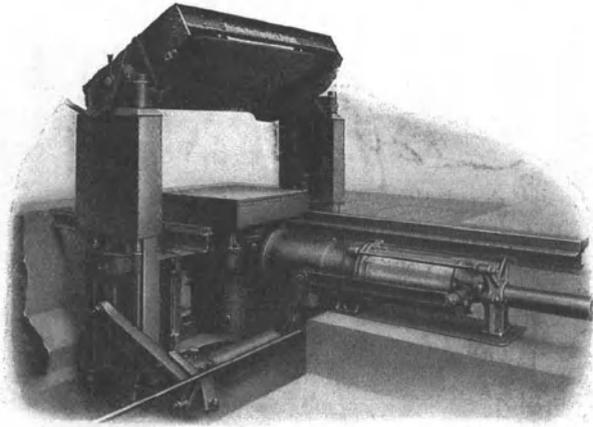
Wendeplatten-Rüttler (Badische Maschinenfabrik).
